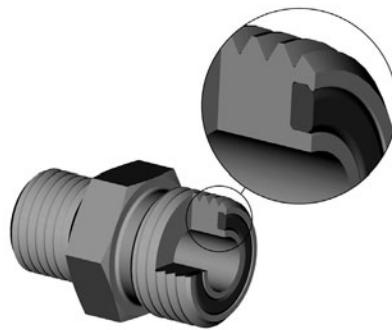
Detalle de Corte de la Ranura O-ring (CORG)
